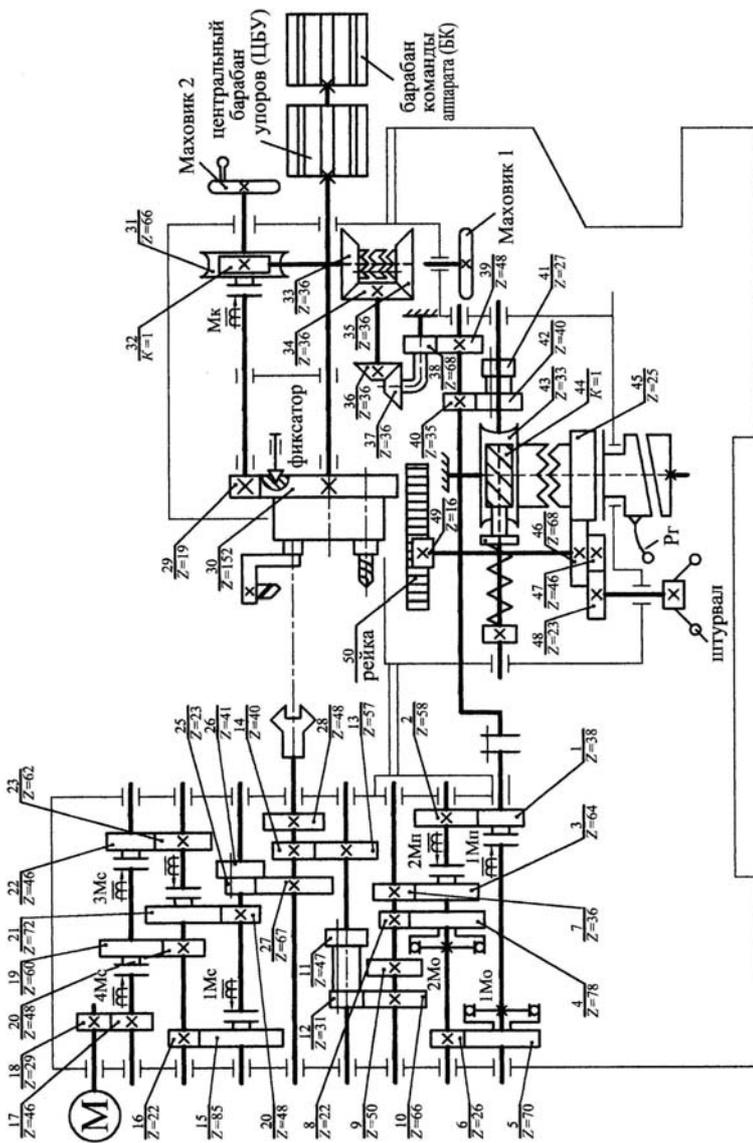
Кинематическая схема токарно-револьверного станка модели 1341
